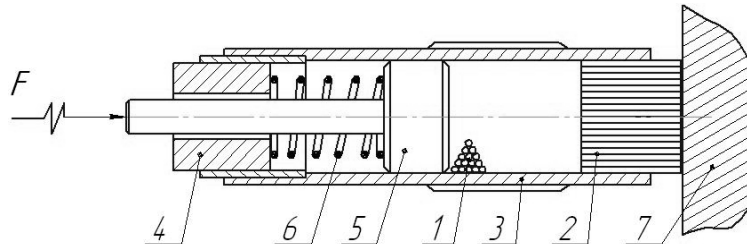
Схема шарико-стержневой упрочнителя: 1 — шариковая среда; 2 — стержни (инструмент); 3 — корпус; 4 — гайка; 5 — боек (поршень); 6 — пружина; 7 — обрабатываемая деталь
